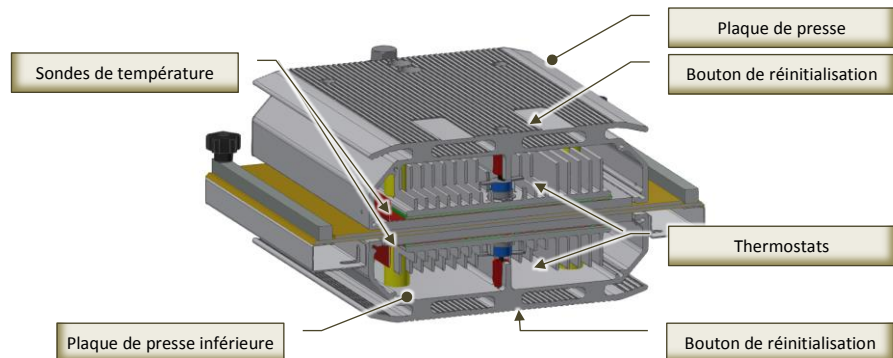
Thermostats de sécurité à réarmement manuel de la machine (vue en coupe de la presse)
